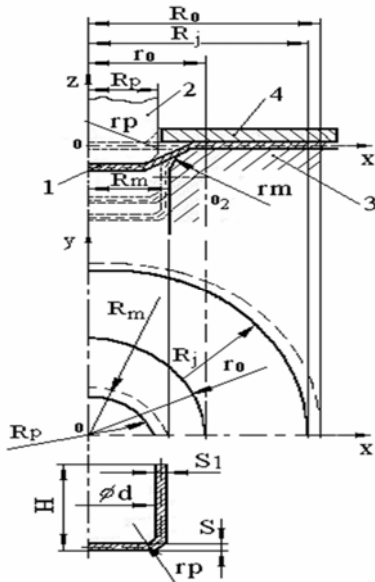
Вытяжка цилиндрической детали из круглой заготовки
